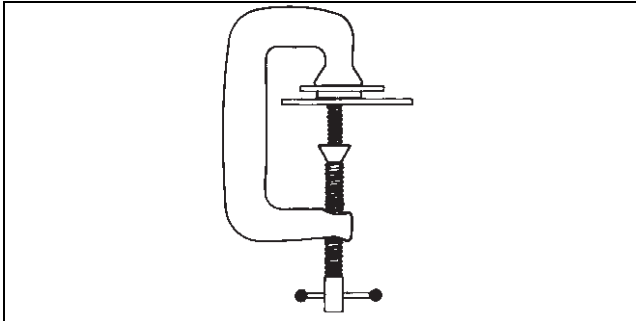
Schraubzwinde mit einer Spiralfeder unter Druck. Die Feder kann entnommen und ihre Kraft als Funktion des Federwegs leicht geprüft werden.
